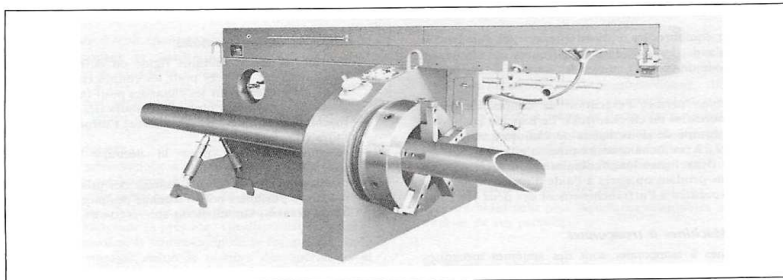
Machine pour la coupe des tubes et l'usinage des extrémités.
